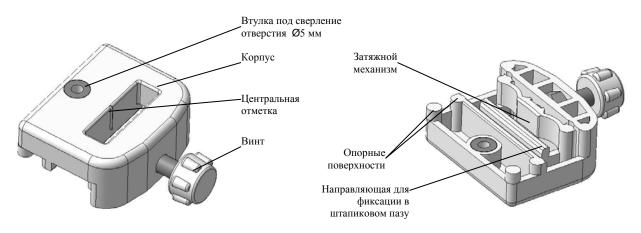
КСИ 246 Кондуктор соединителя импоста.
